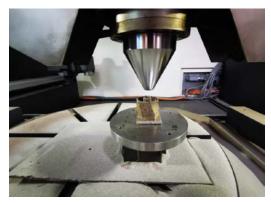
3D-принтер для лазерной наплавки металла, приспособленный учеными из Сколтеха к печати металлической пены
